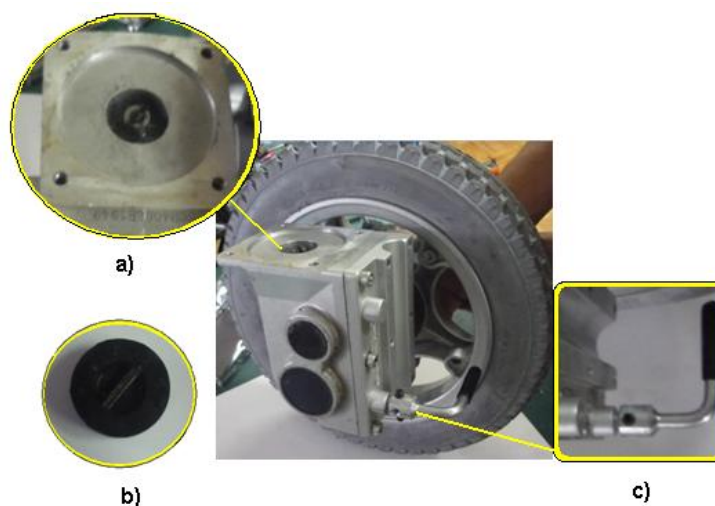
Componentes de la caja reductora; a) Cara de acoplamiento de la caja reductora, b) Eje de acoplamiento del motor con la caja reductora, c) Embrague
